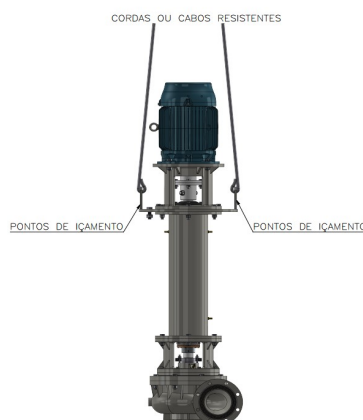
Desenho esquemático para fixação e içamento do conjunto moto-bomba no transporte do mesmo para sua instalação, observando-se a fixação por cordas ou cabos resistentes em pontos extremos do conjunto, na base metálica ou ainda no próprio conjunto (bomba e motor).
